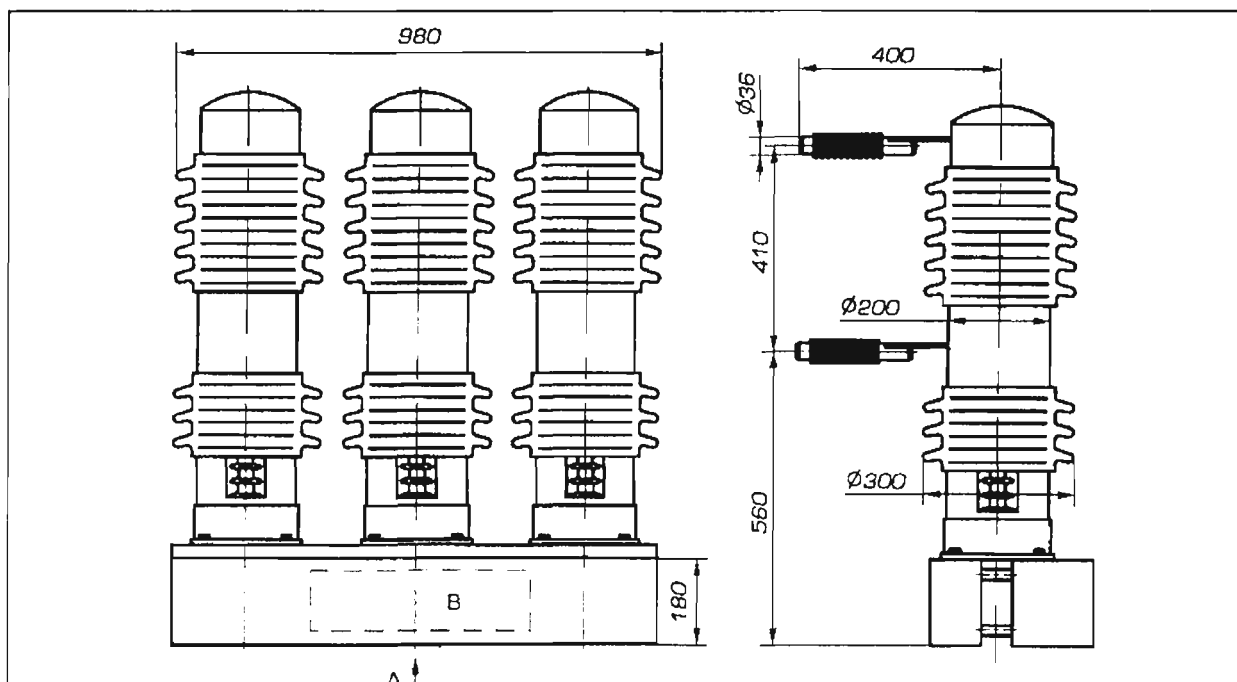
Габаритные размеры выключателя ВВСВ-35-25/630-1600
